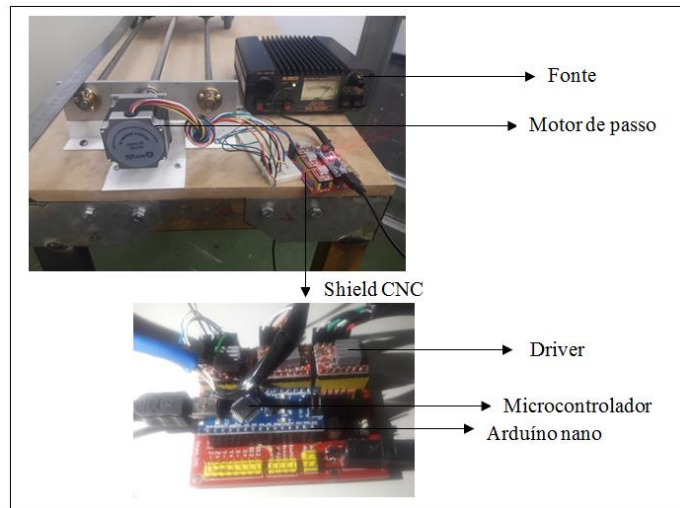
Fonte, motor de passo e *CNC Shield*.
